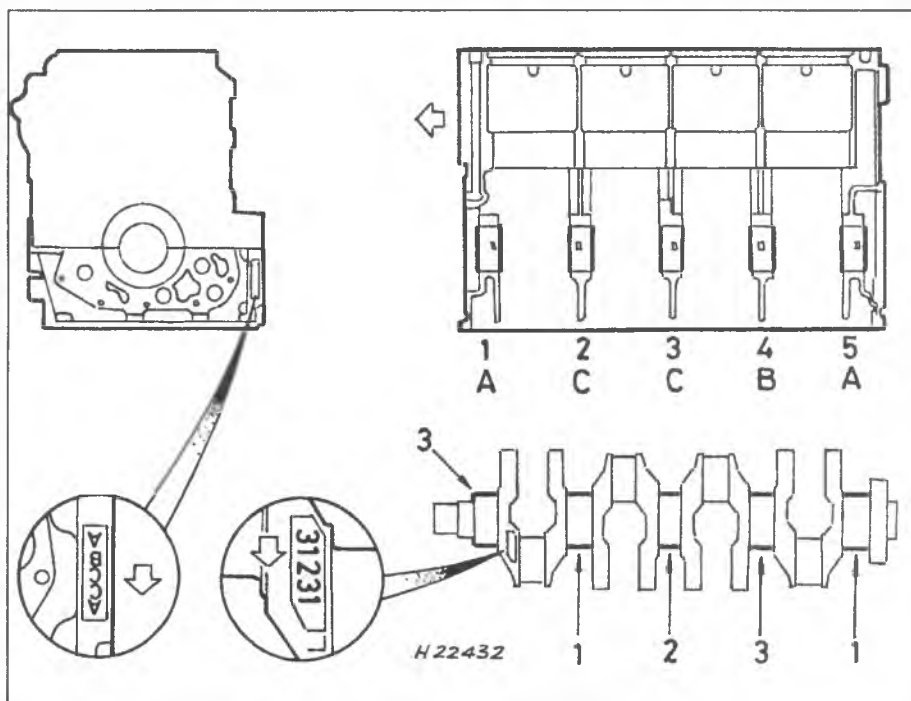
Расположение кодов размерных групп коренных подшипников на коленчатом вале и блоке цилиндров – бензиновый двигатель
